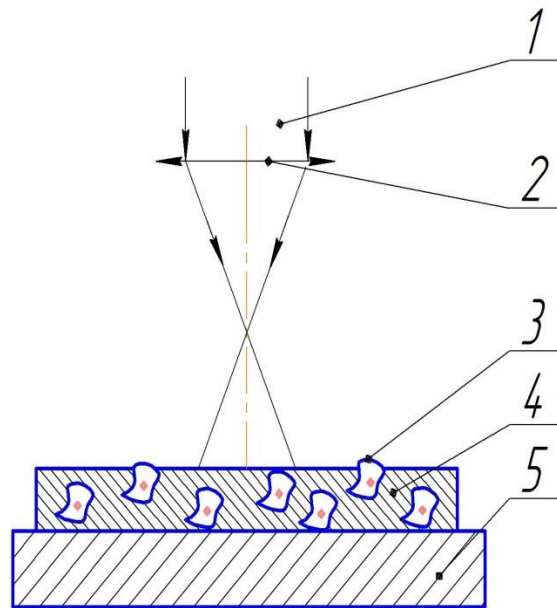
Способи формування робочої частини інструменту шляхом пошарового лазерного спікання композиту
